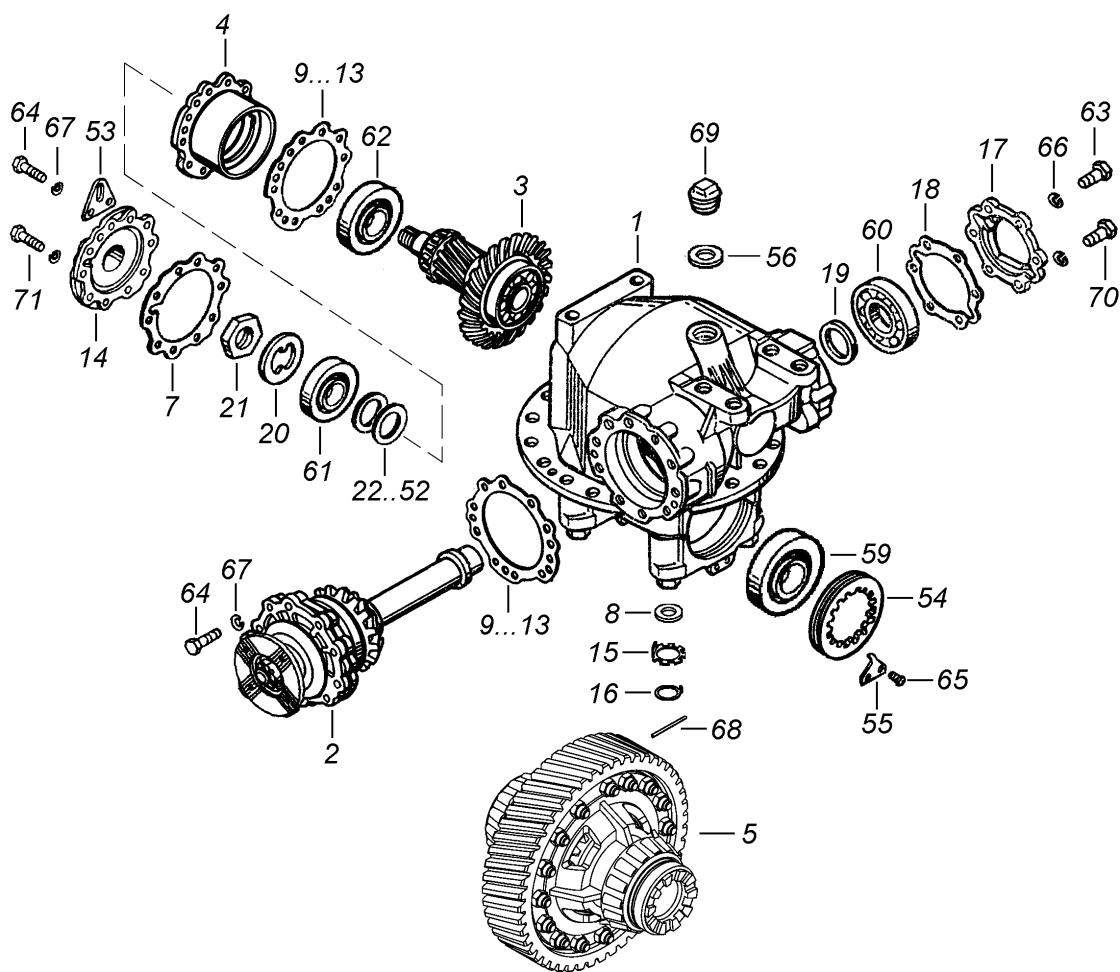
Устройство заднего редуктора КАМАЗ
